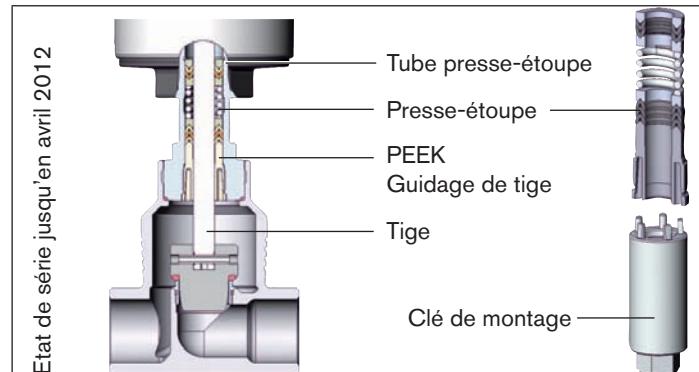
Remplacement du presse-étoupe (PEEK guidage de tige)
